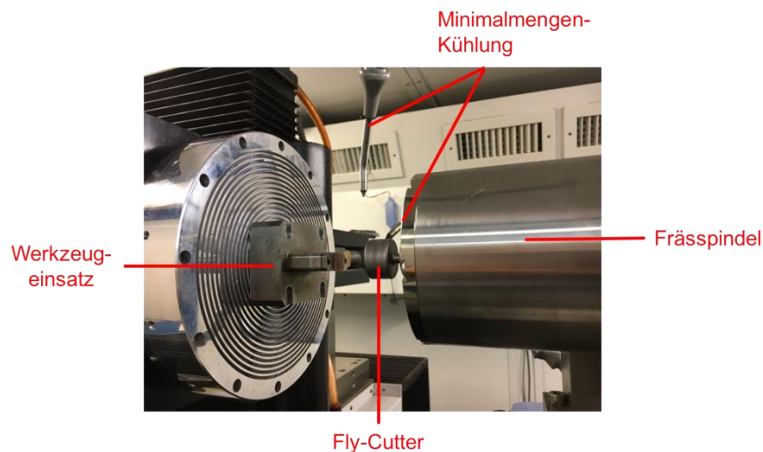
Fly-Cutting-Bearbeitung des Werkzeugeinsatzes
